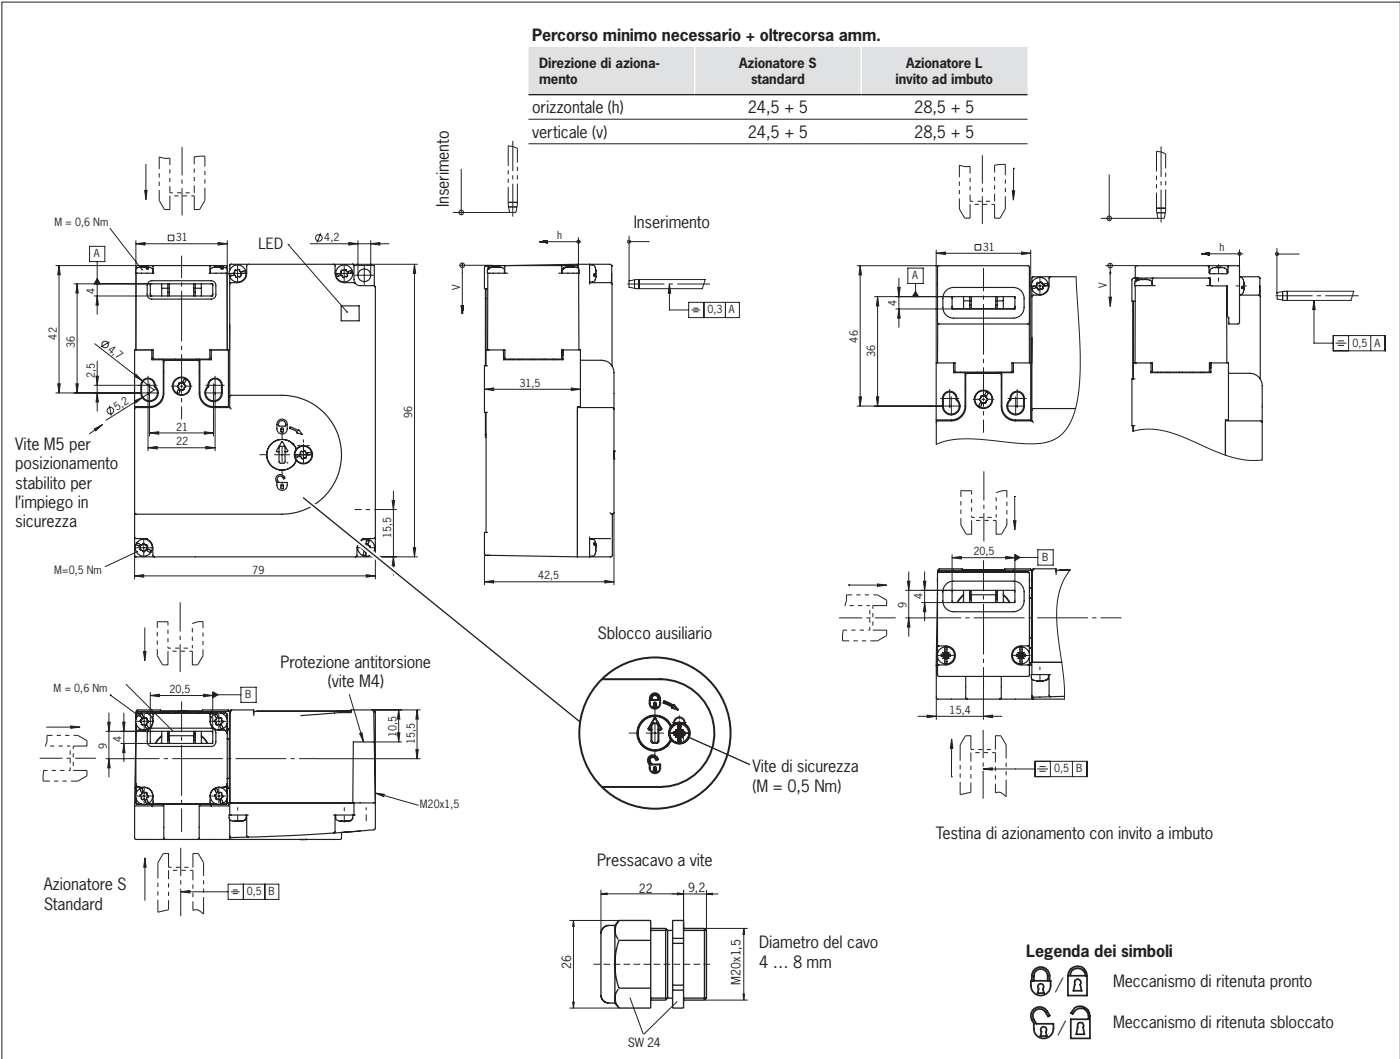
Dimensioni STM Pro senza invito ad imbuto e STM Pro con invito ad imbuto
